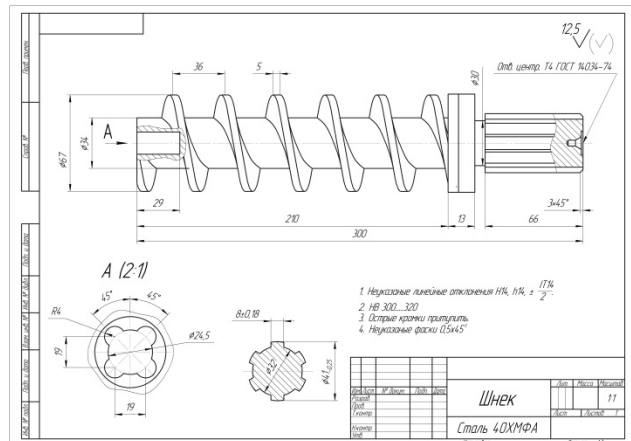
Креслення модернізованого шліцьового шнека, виготовленого методом механічної обробки
